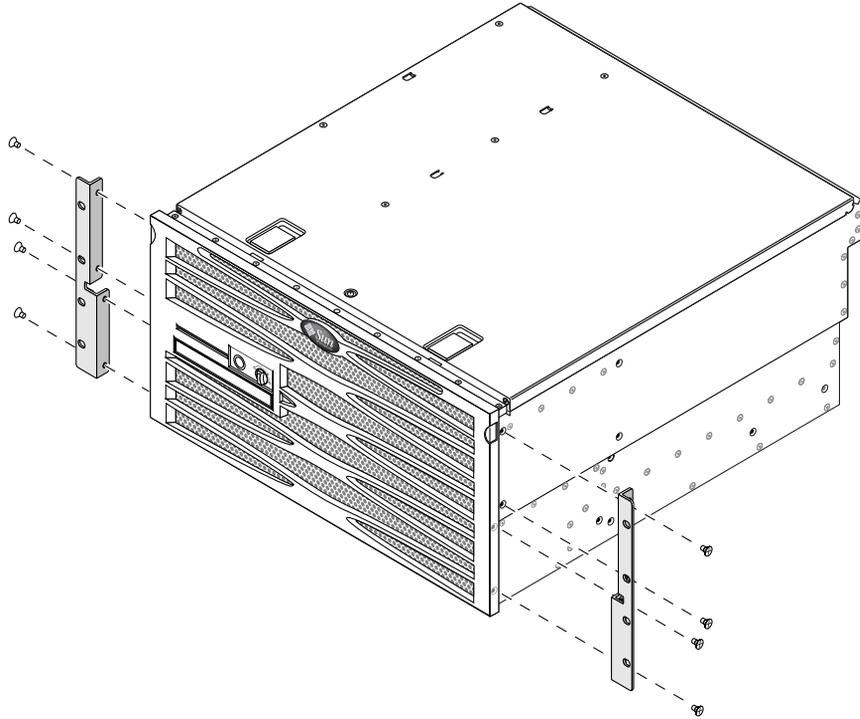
Fijación de los soportes de montaje fijo al servidor
